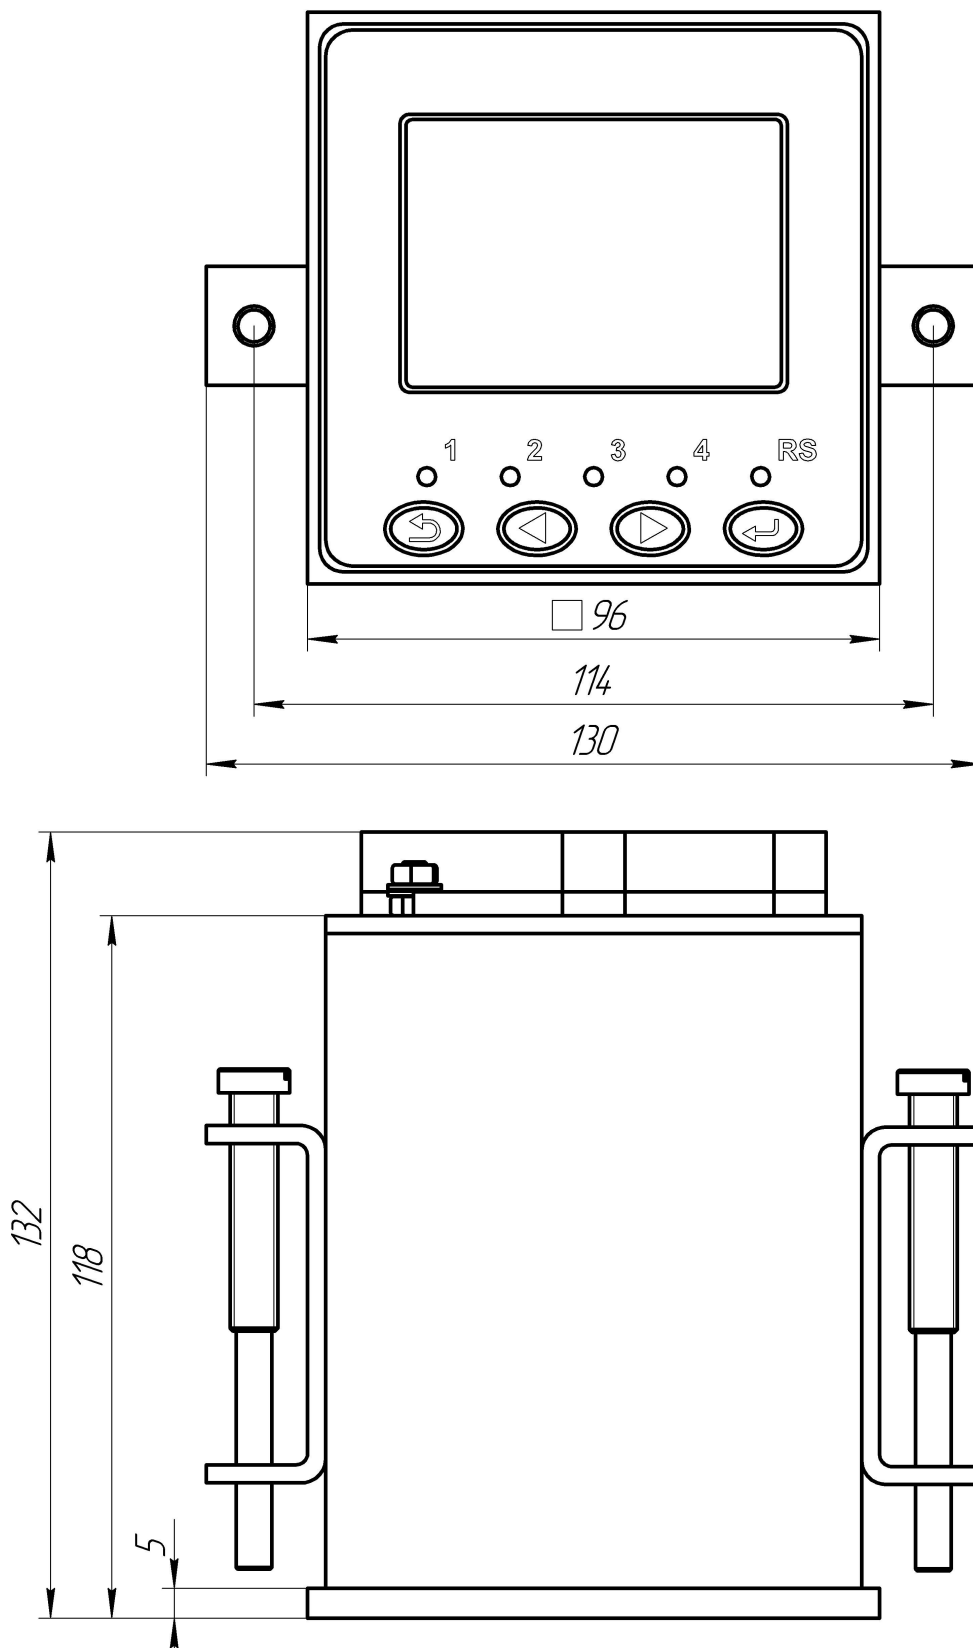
Габаритные размеры контроллера щитового исполнения
